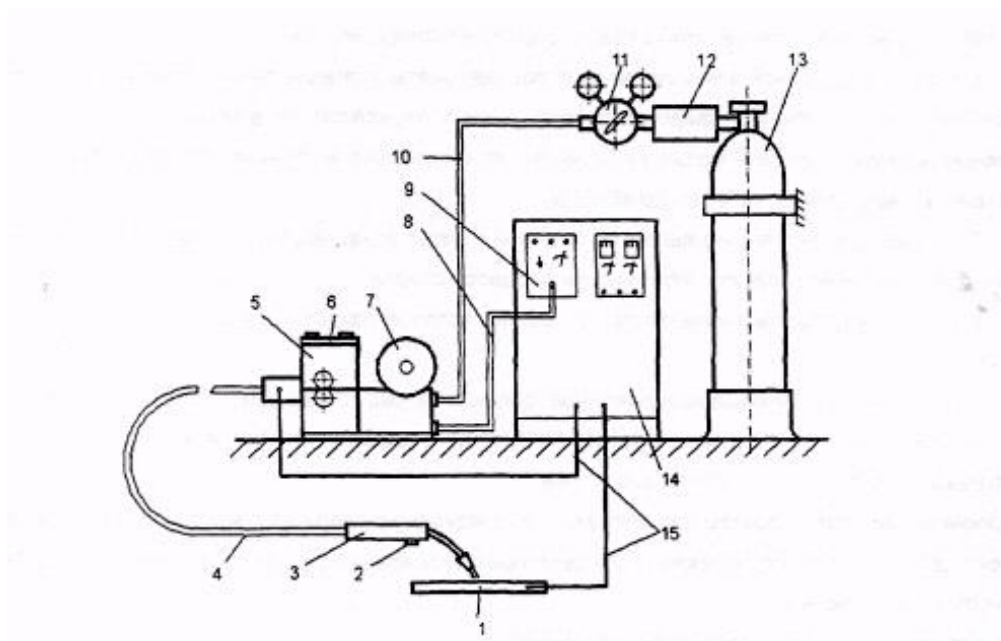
Установка для дуговой механизированной сварки в CO₂-газе:
